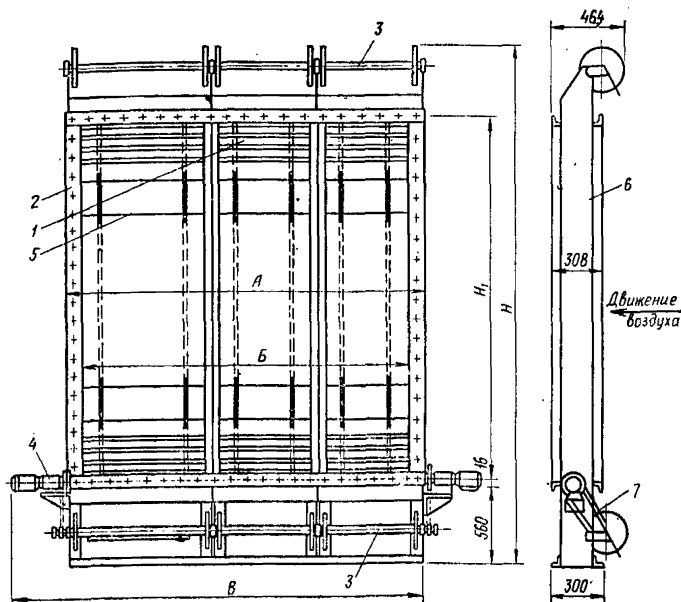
Габаритный чертеж фильтра ФРУ (ФРУА и ФРУБ)
